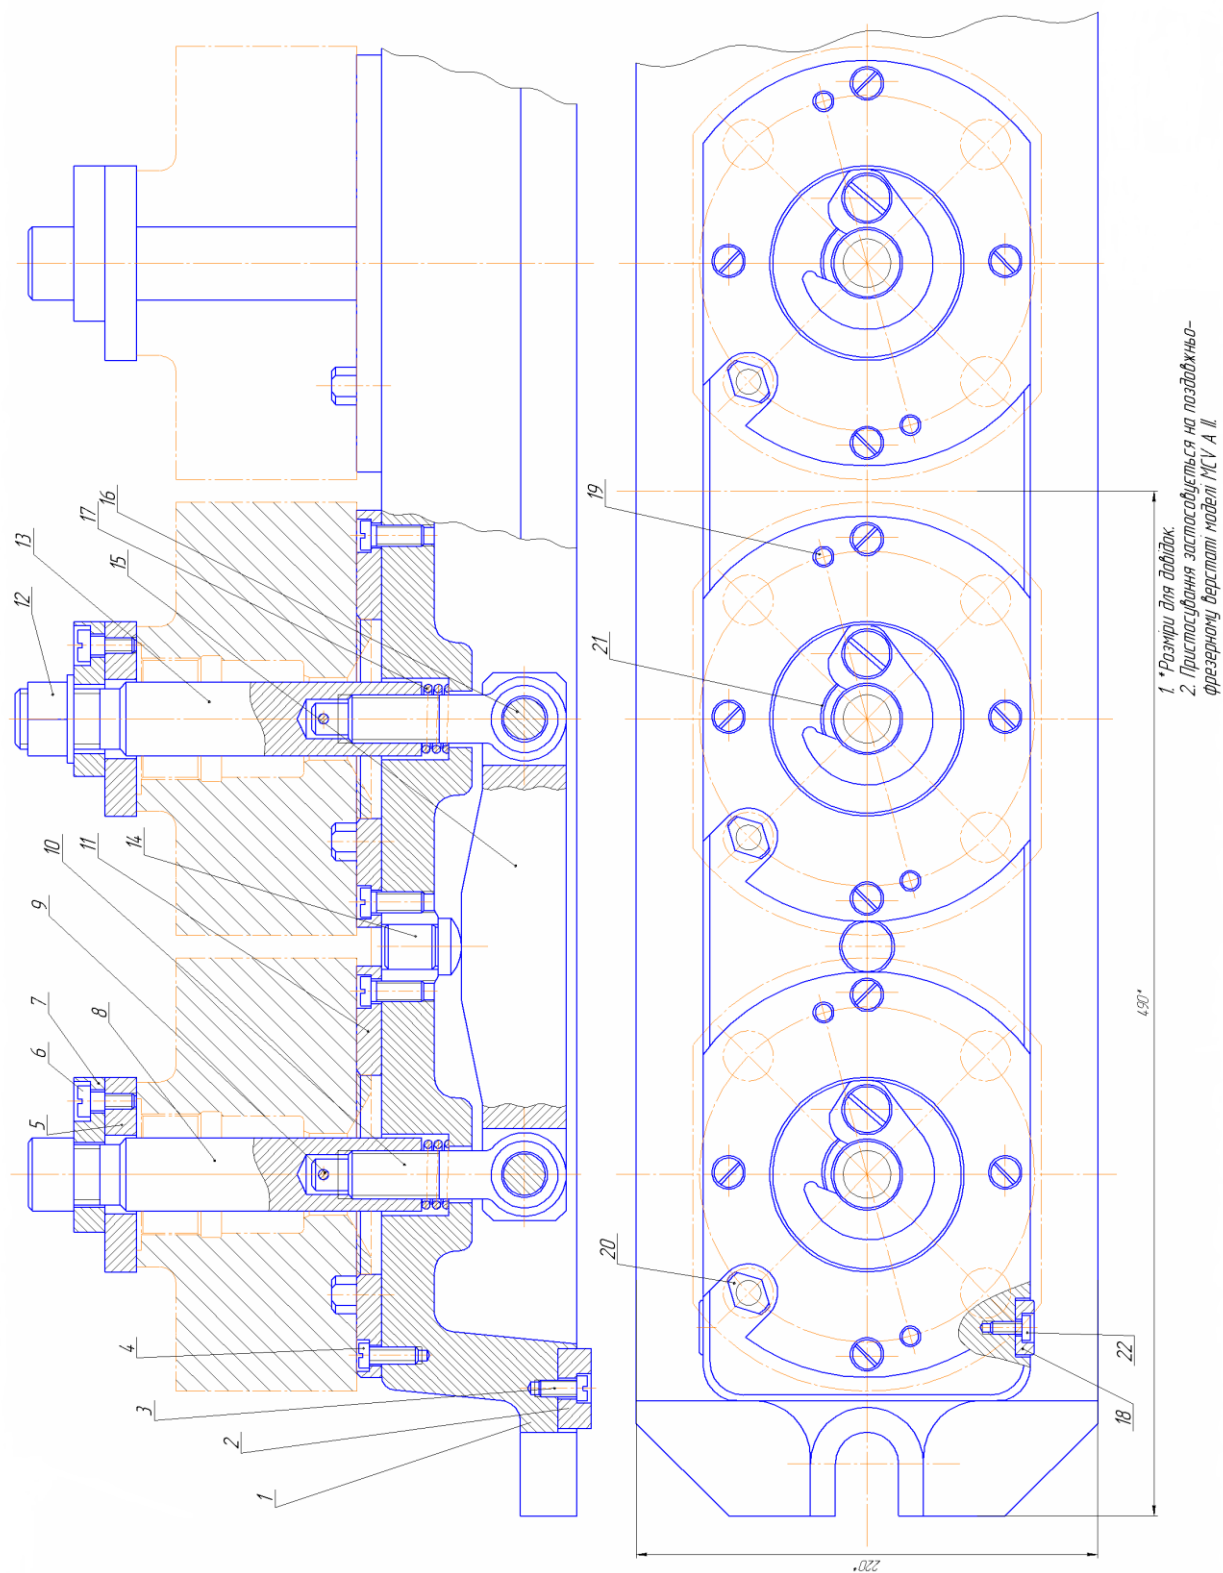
пристосування для фрезерування декілька поверхонь одночасно
